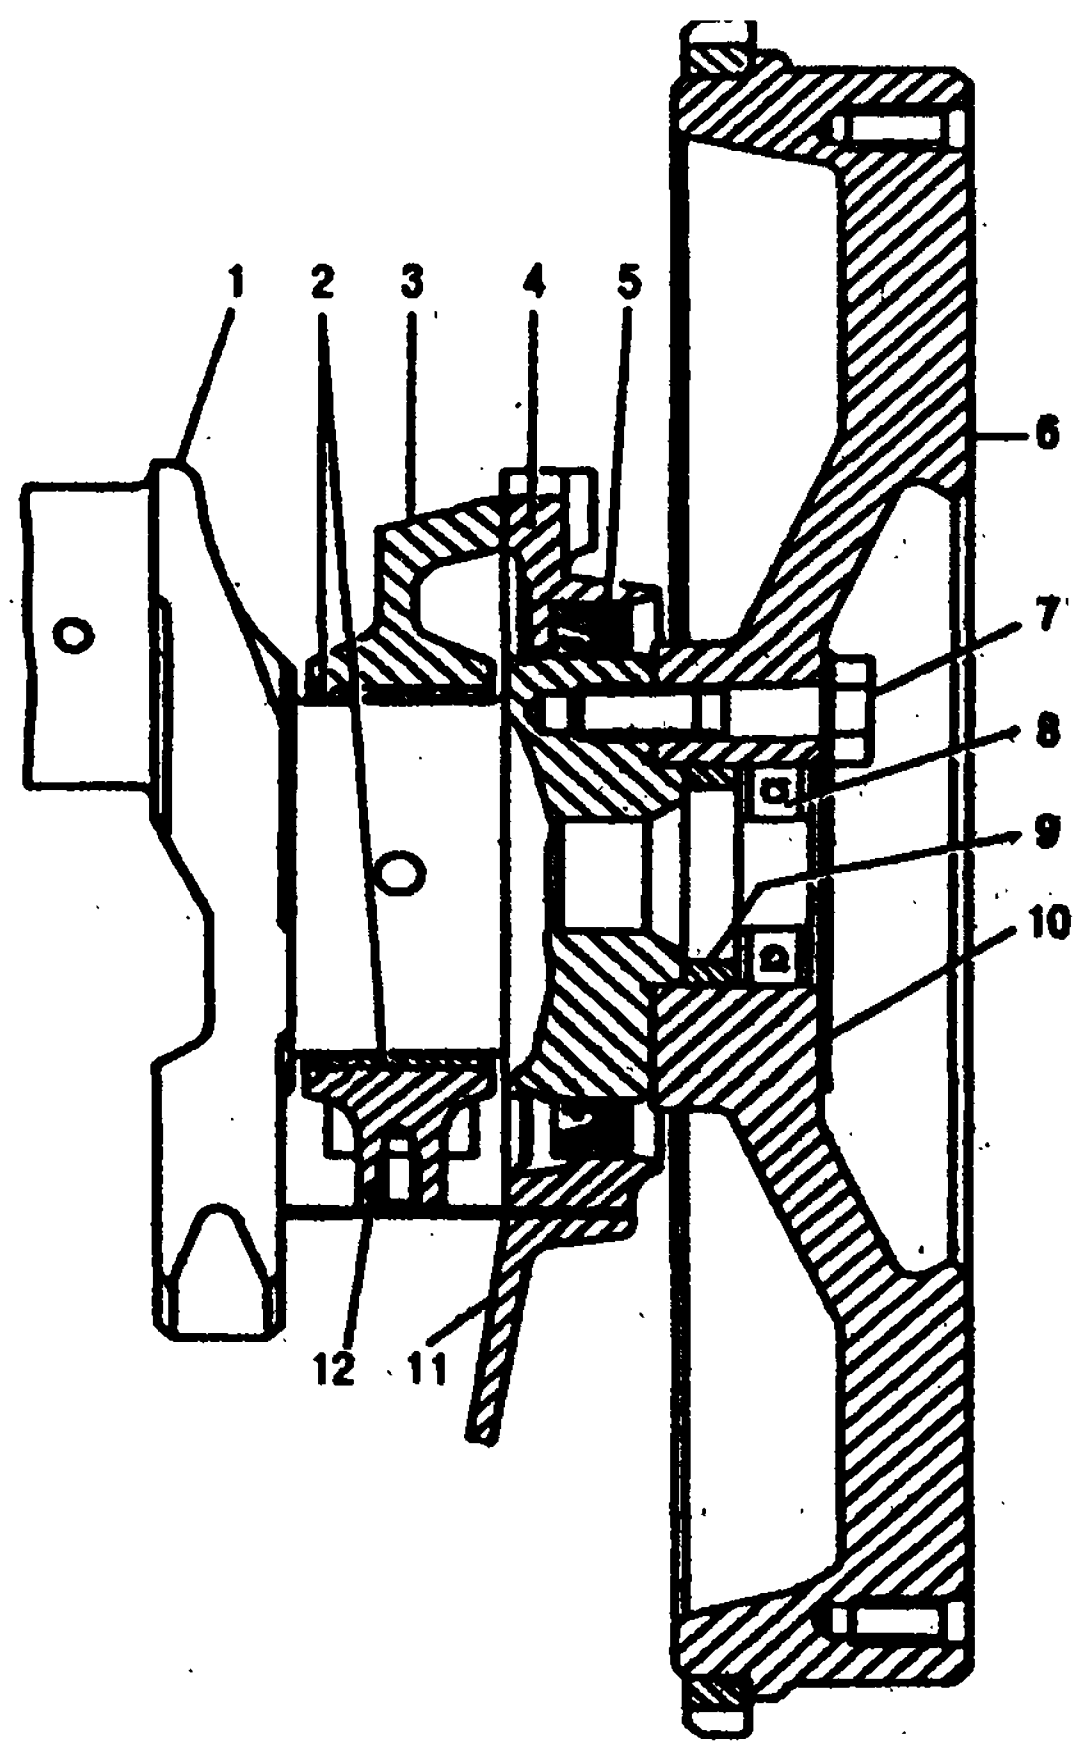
Задний конец коленчатого вала: 1 - коленчатый вал; 2 - вкладыши подшипника; 3 - блок цилиндров; 4 - крышка; 5 - манжета; 6 - маховик; 7 - болт крепления маховика; 8 - подшипник; 9 - распорная втулка; 10 - шайба болтов маховика; 11 - масляный картер; 12 - крышка подшипника
